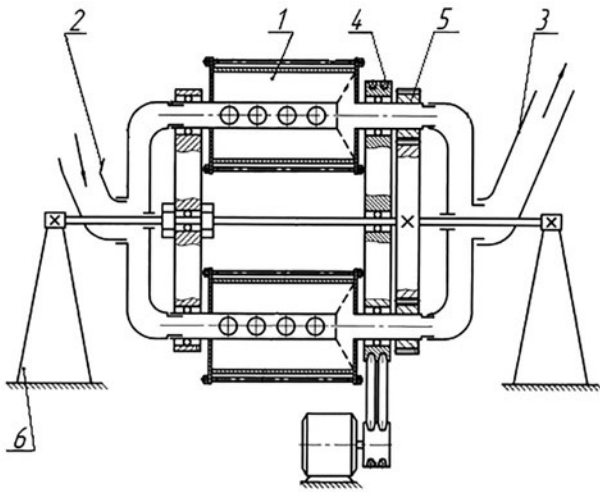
Горизонтальная планетарная мельница с внешней обкаткой: 1 — помольный барабан; 2 — загрузочная воронка; 3 — разгрузочный патрубок; 4 — ременной привод; 5 — водило; 6 — опора
